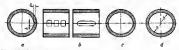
Eliminación del rozamiento elevado en las juntas da los casquillos
